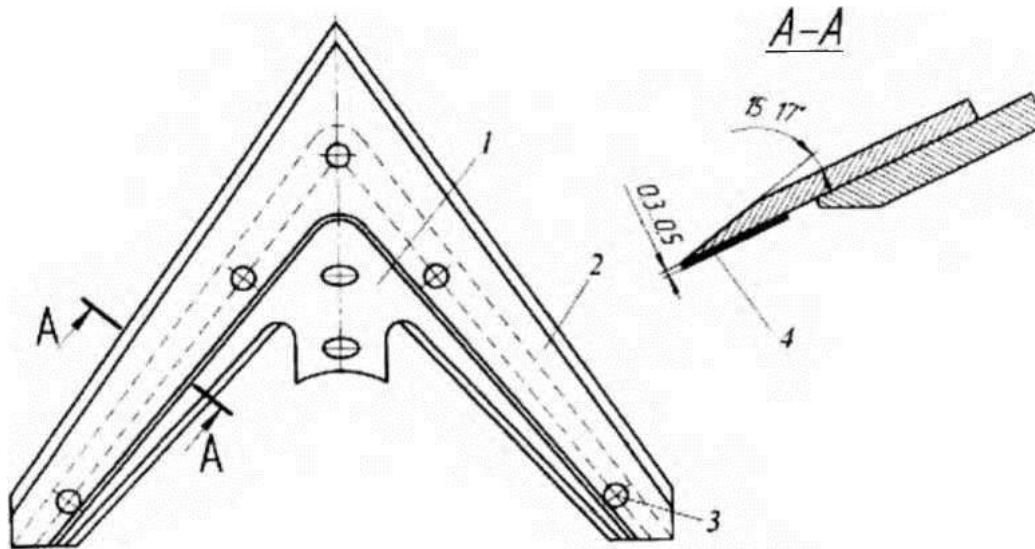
Робочий орган культиватора [9], вид зверху
